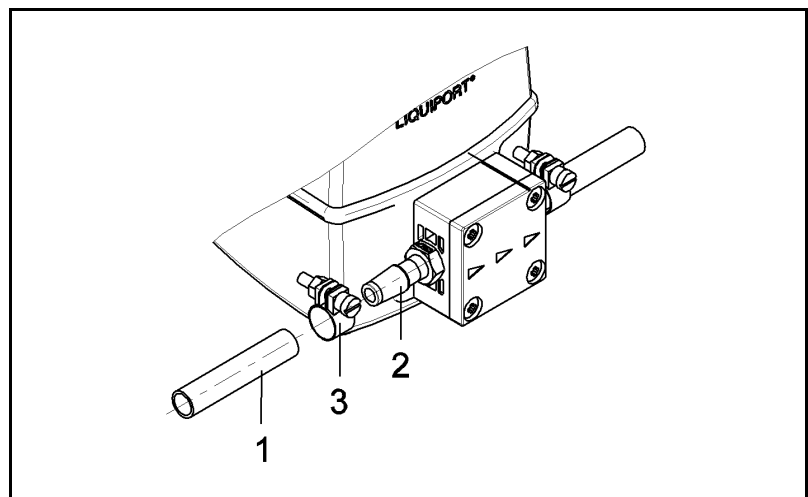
Tubulure ID 8 mm ou ID 12 mm
